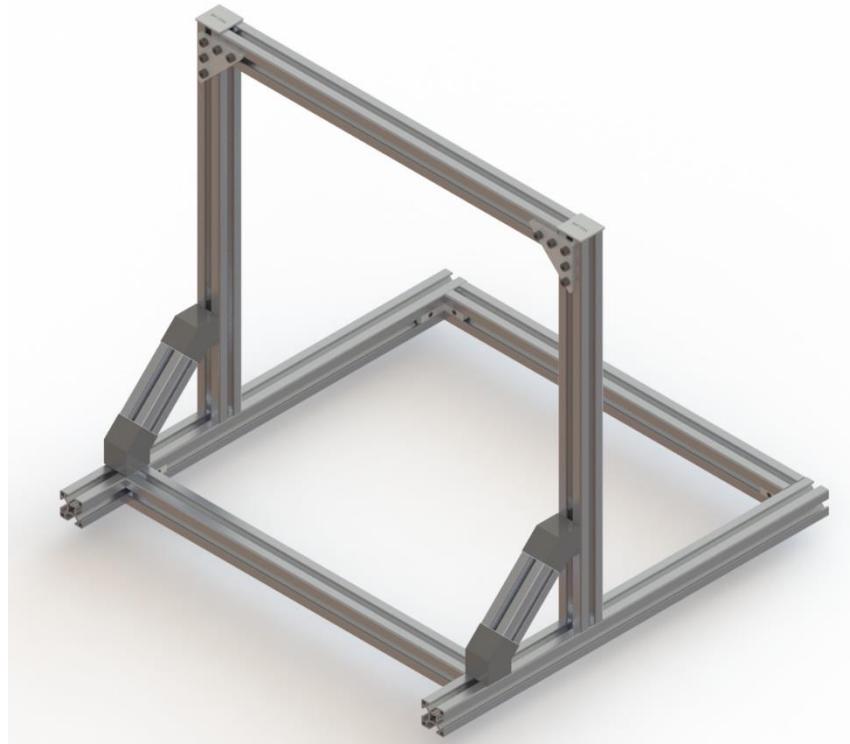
Ensamblaje de estructura; Fuente: Elaboración propia con SW
